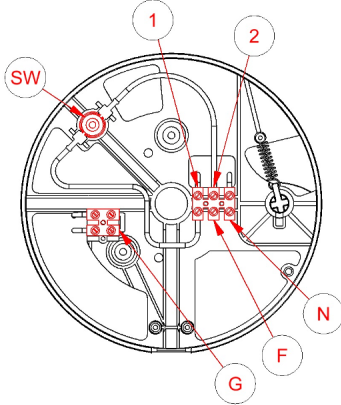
4 KABEL ohne Thermoschutzschalter
